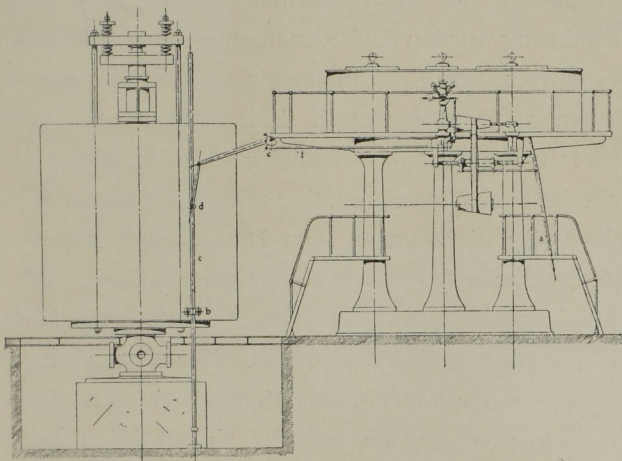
Ansicht der Pumpmaschine und des Kraftsammlers.
